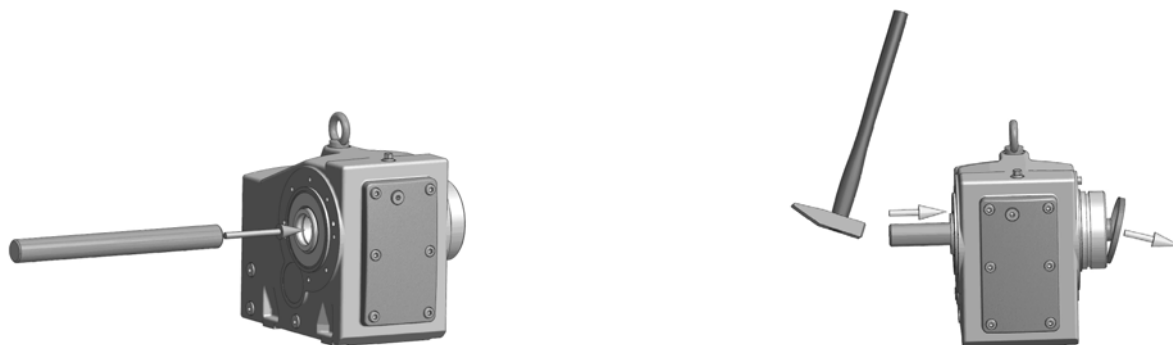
Desmontaje de la caperuza de cierre montada de fábrica
